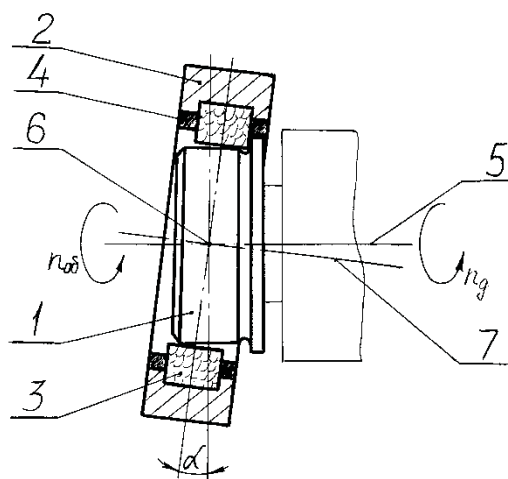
Схема способа имитационной безабразивной обработки дорожек качения колец роликоподшипников
